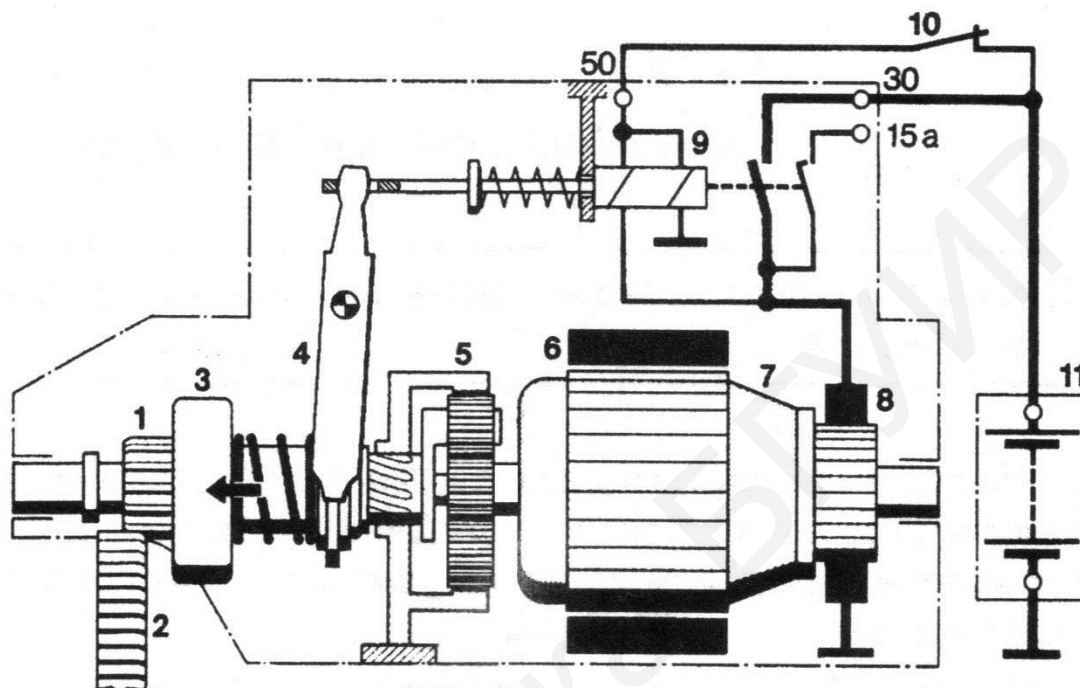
Схема стартера Bosch DW с постоянными магнитами и понижающей передачей:
